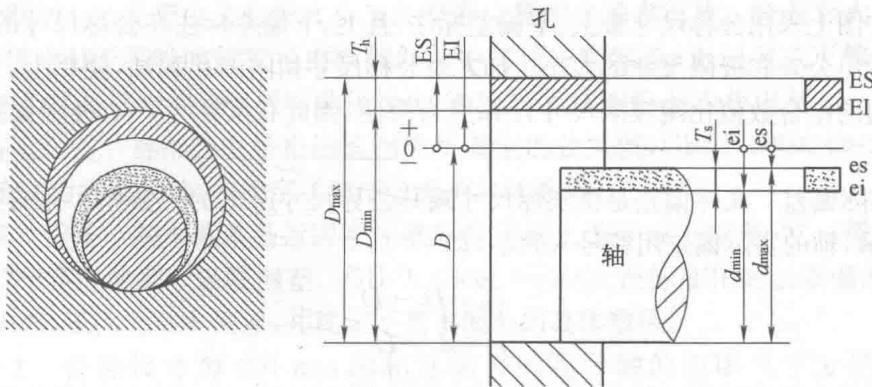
公称尺寸、极限尺寸和极限偏差、尺寸公差
